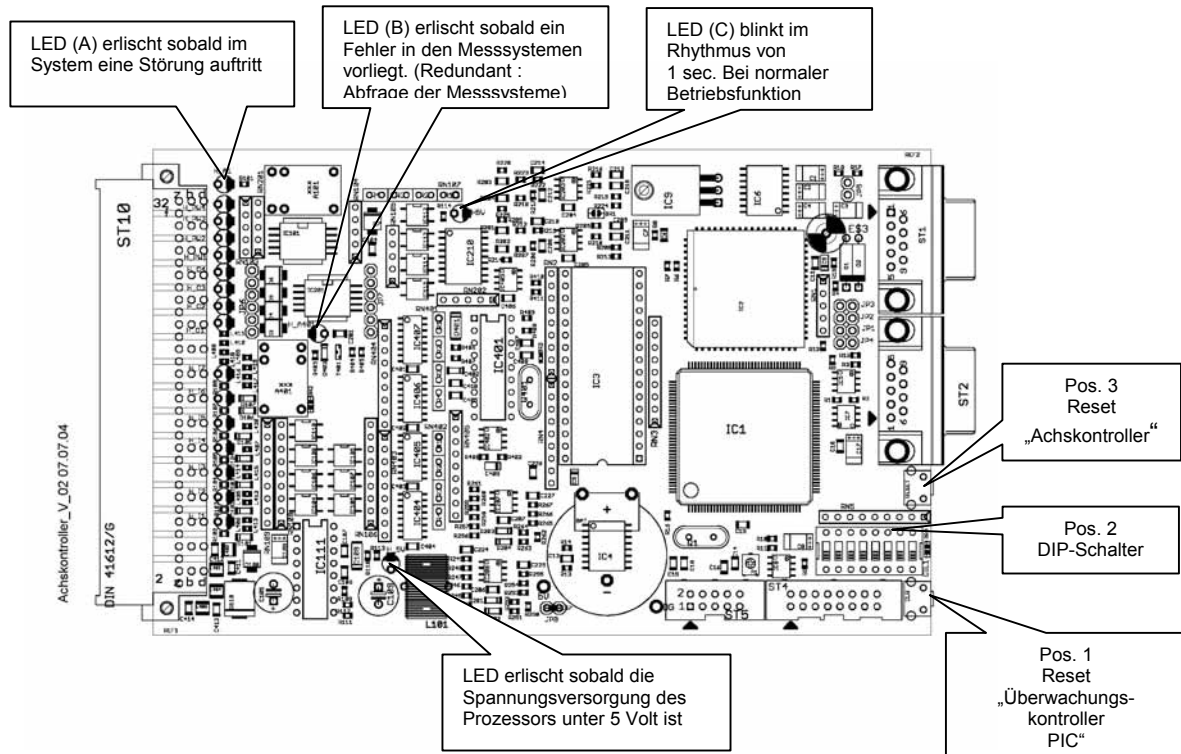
DIP-Schalter auf der Platine im Elektrokasten.
